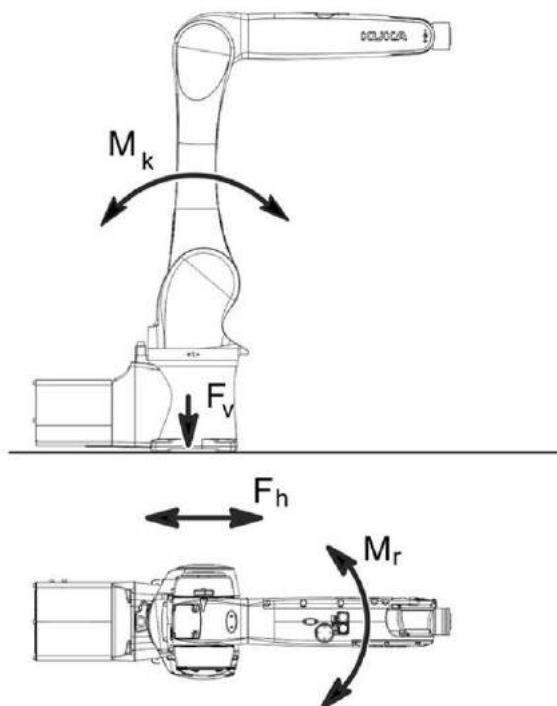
Нагрузки, действующие на фундамент, напольный монтаж
